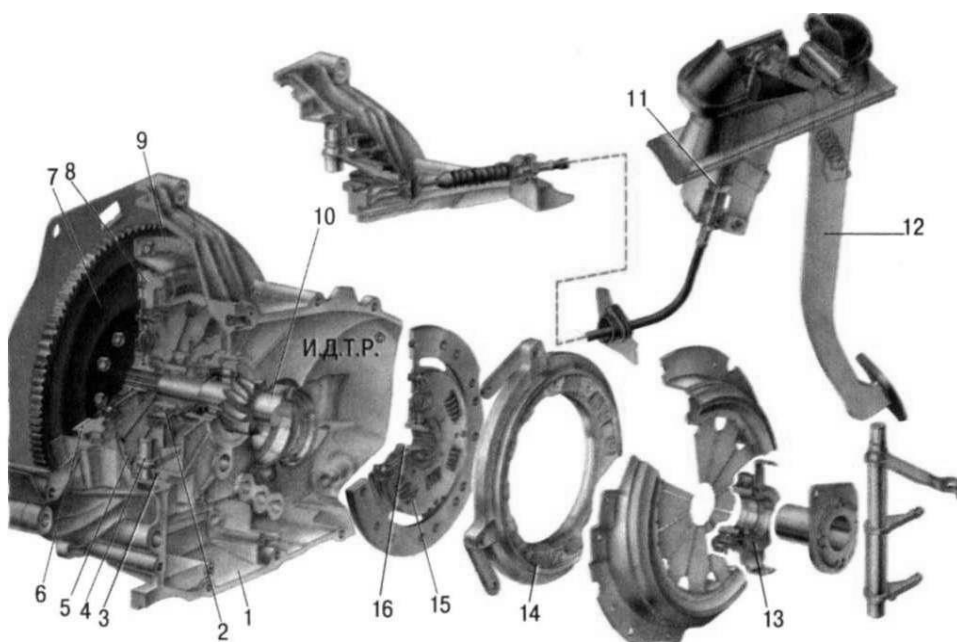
Сцепление: 1 - картер сцепления; 2 - подшипник выключения сцепления; 3 - втулка опорная вала вилки выключения сцепления; 4 - вилка выключения сцепления; 5 - нажимная пружина; 6 - ведомый диск; 7 - маховик; 8 - нажимной диск; 9 - кожух сцепления; 10 - первичный вал коробки передач; 11 - трос; 12 - педаль сцепления; 13 - муфта подшипника выключения сцепления; 14 - пластина, соединяющая кожух сцепления с нажимным диском; 15 - пружина демпфера; 16 - ступица ведомого диска
